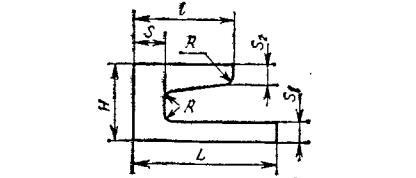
Горячепрессованный профиль из латуни ЛС59-1 (ТУ 48-21-135-72)
